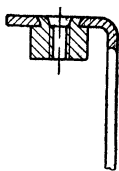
Резьбовая втулка, развальцованная в полке несущей части корпуса прибора
